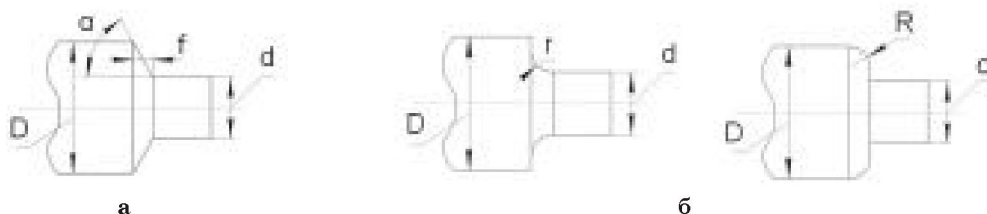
Конструктивні виконання насадок дозувального пристрою: а) із фаскою різної величини при основі насадки; б) із заокругленням при основі насадки
